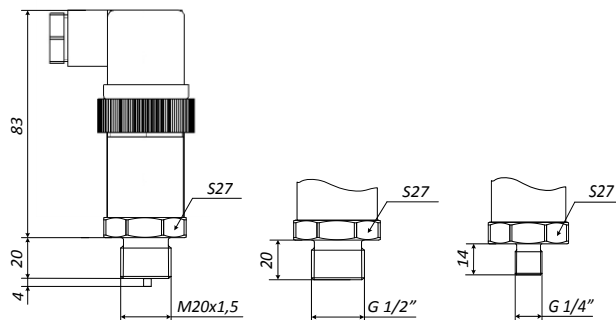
Габаритные и присоединительные размеры датчика.
